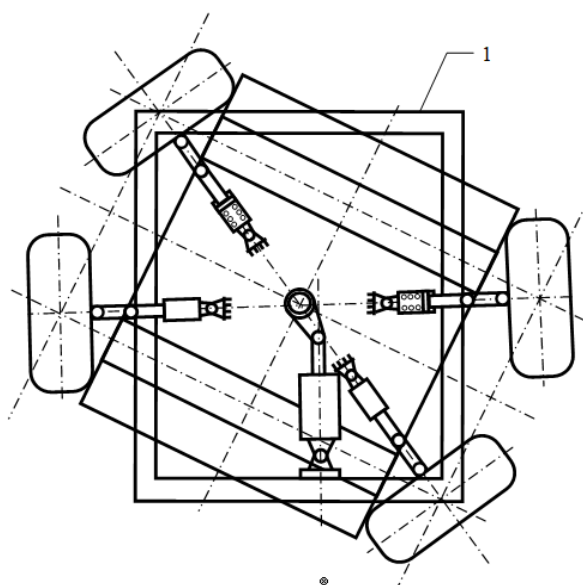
Положення поворотної платформи після закінчення повороту
